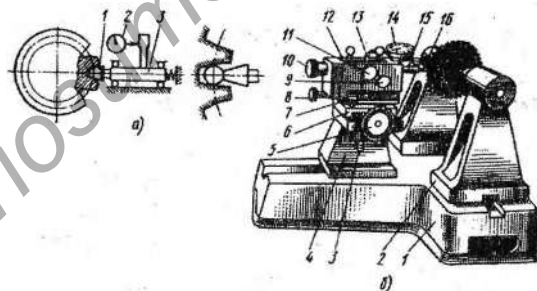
Биеннемер Б-10М: а — схемы измерения: 1 — измерительный наконечник, 2 — измерительная головка, 3 — каретка; б — внешний вид: 1 — станина, 2 — центровые бабки, 3, 7, 10 — винты, 4 — бабка, 5, 9 — маховики, 6 — каретка, 8, 11 — ручки, 12 — измерительный узел, 13 — планка, 14 — наконечник индикатора, 15 — шток, 16 — наконечник [10, с. 306]
